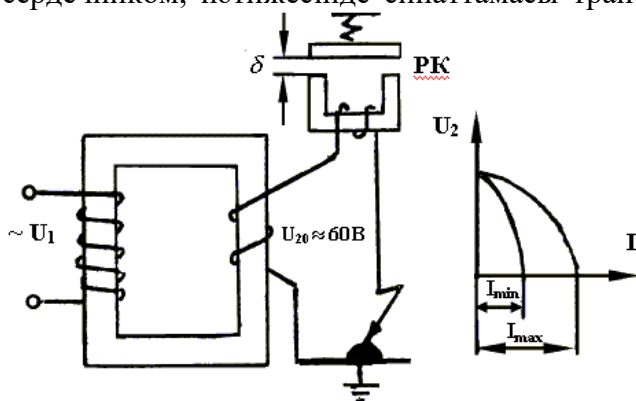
Сварочный трансформатор
